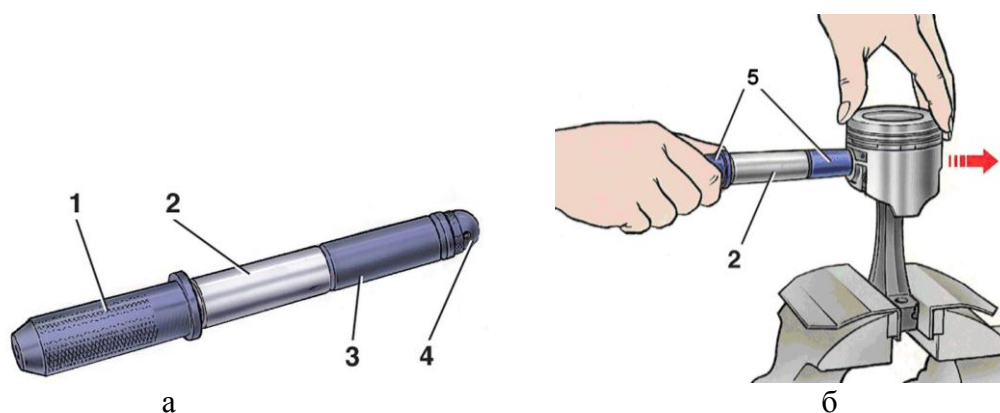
Запрессовка поршневого пальца в верхнюю головку шатуна: а – приспособление; б – процесс запрессовки; 1 – валик приспособления; 2 – поршневой палец; 3 – направляющая; 4 – упорный винт; 5 – приспособление
